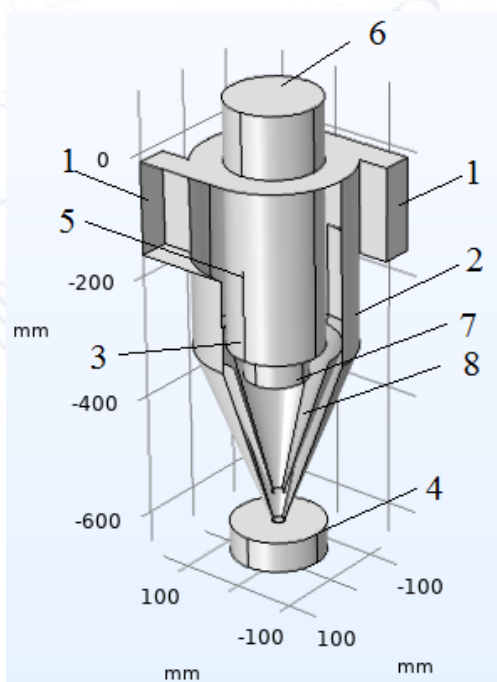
Модифицированный центробежный пылеуловитель. 1-вход в спиральный воздухо-заборник, 2- цилиндрический корпус пылеуловителя, 3- конусный корпус пылеуловителя, 4-бункер, 5- труба для отвода очищенного воздуха, 6-выход очищенного воздуха. 7-стабилизатор потока, 8-внутренний конус.
